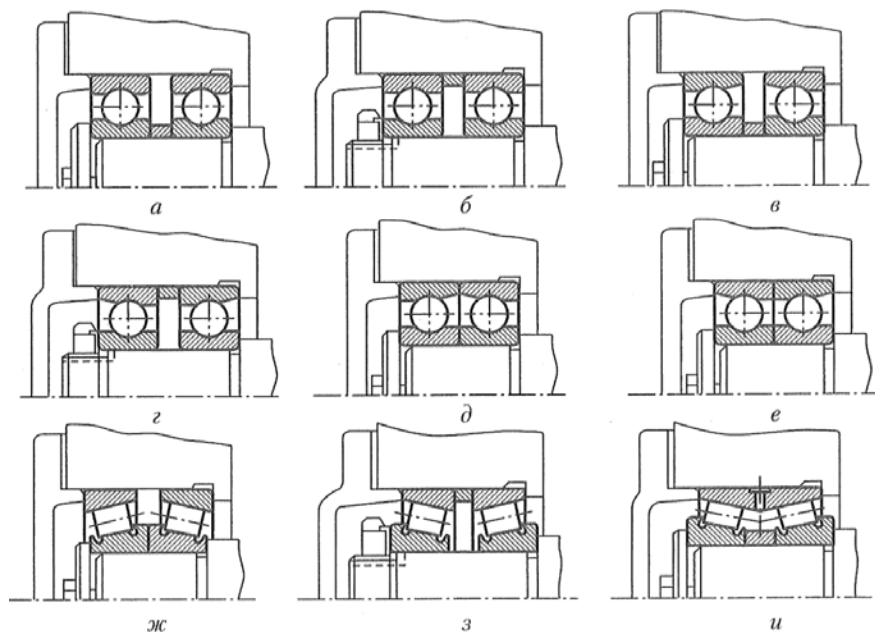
Типы подшипников и схемы их установки в фиксирующей опоре с двумя подшипниками
